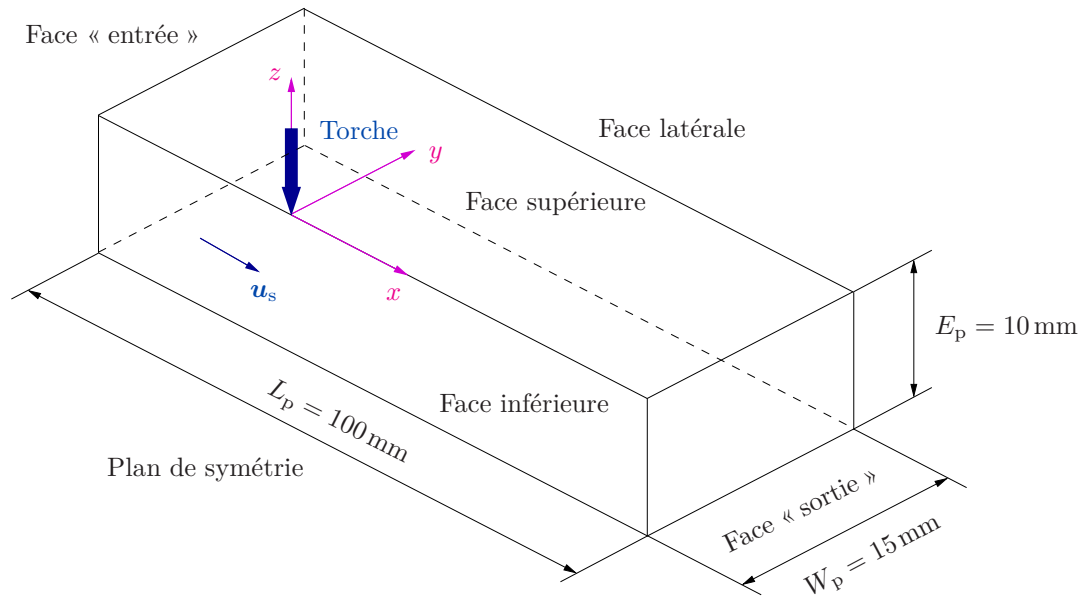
Schéma montrant la désignation des faces sur la géométrie avec défilement de la torche de soudage.
